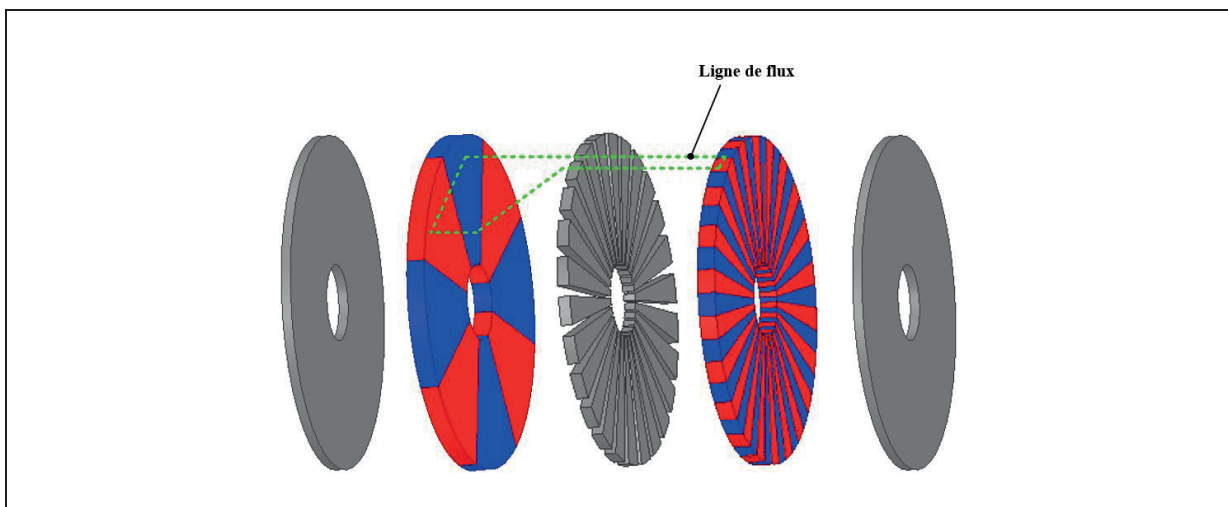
Vue en éclaté de l'engrenage magnétique coaxial à flux axial
